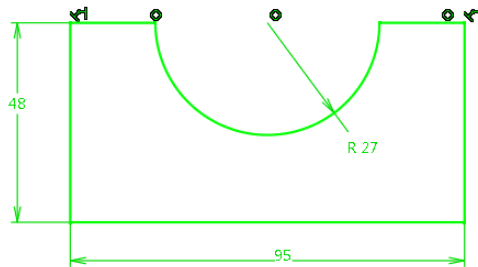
Einfachster Fall: 2D-Skizze als Grundlage für 3D-Geometrie
